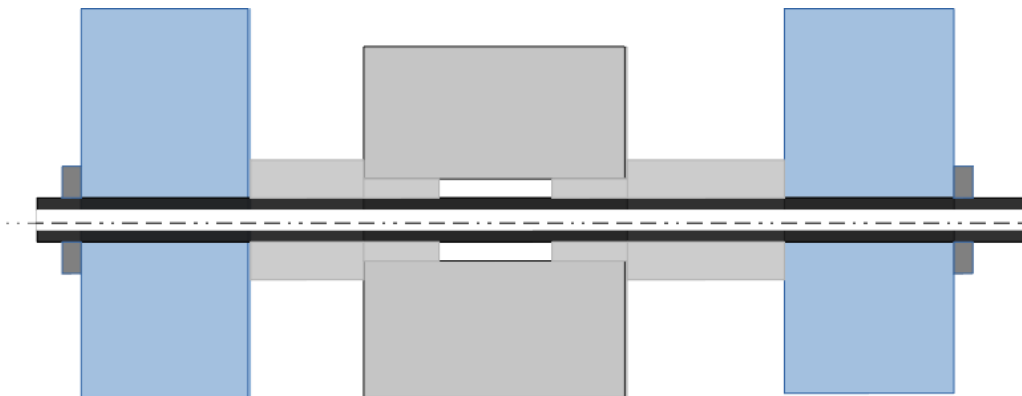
esquema de la primera alternativa para el eje delantero.
